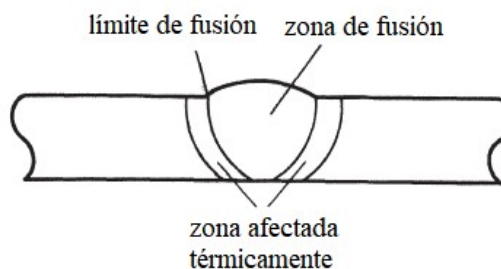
Soldadura por fusión (*Metallurgy of Welding* pág. 7 modificado)
